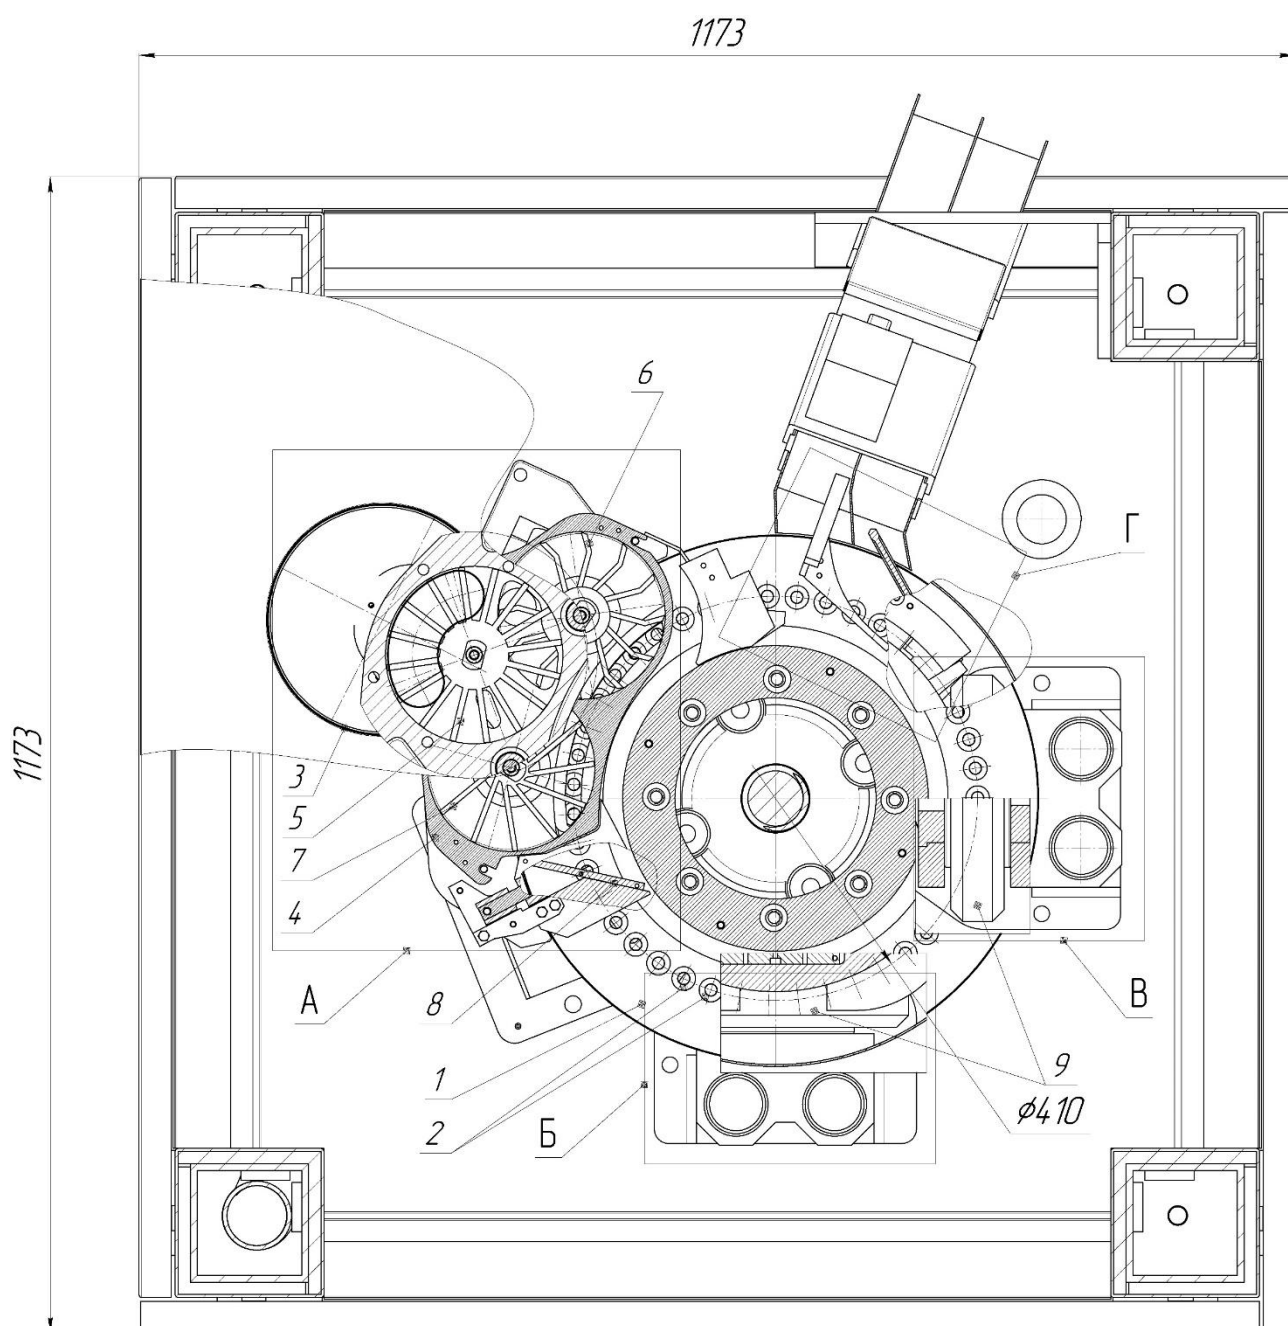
Принципова схема машини (вид зверху з місцевими розрізами)
